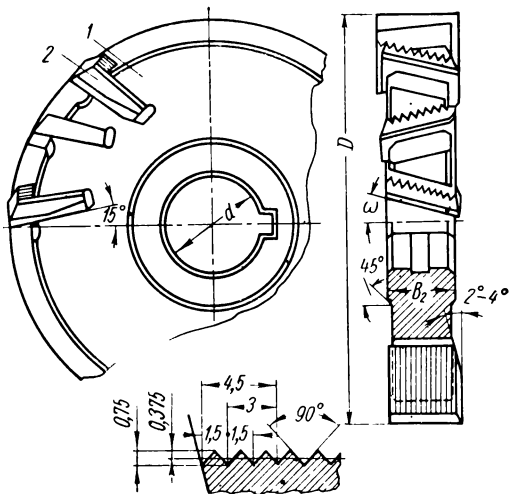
Крепление клиновидных ножей с радиальными рифлями в корпусе дисковой фрезы (конструкция по ГОСТу 1669—59):
